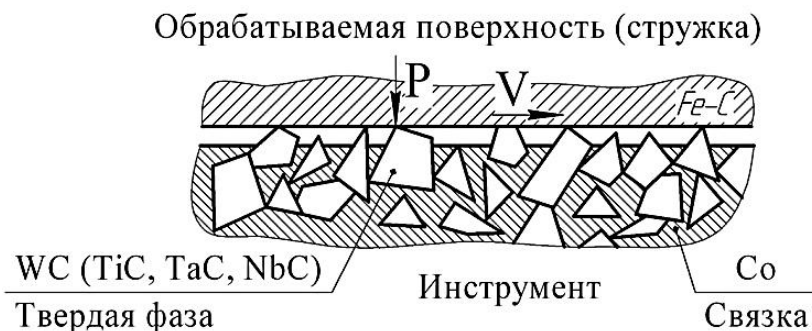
Схема контакта обрабатываемой поверхности и рабочей поверхности твердосплавного инструмента
